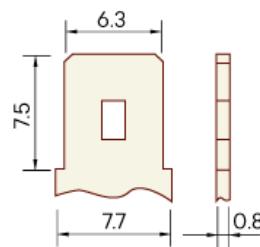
Внешний вид и габаритные размеры выводов подключения внутренних АБ
